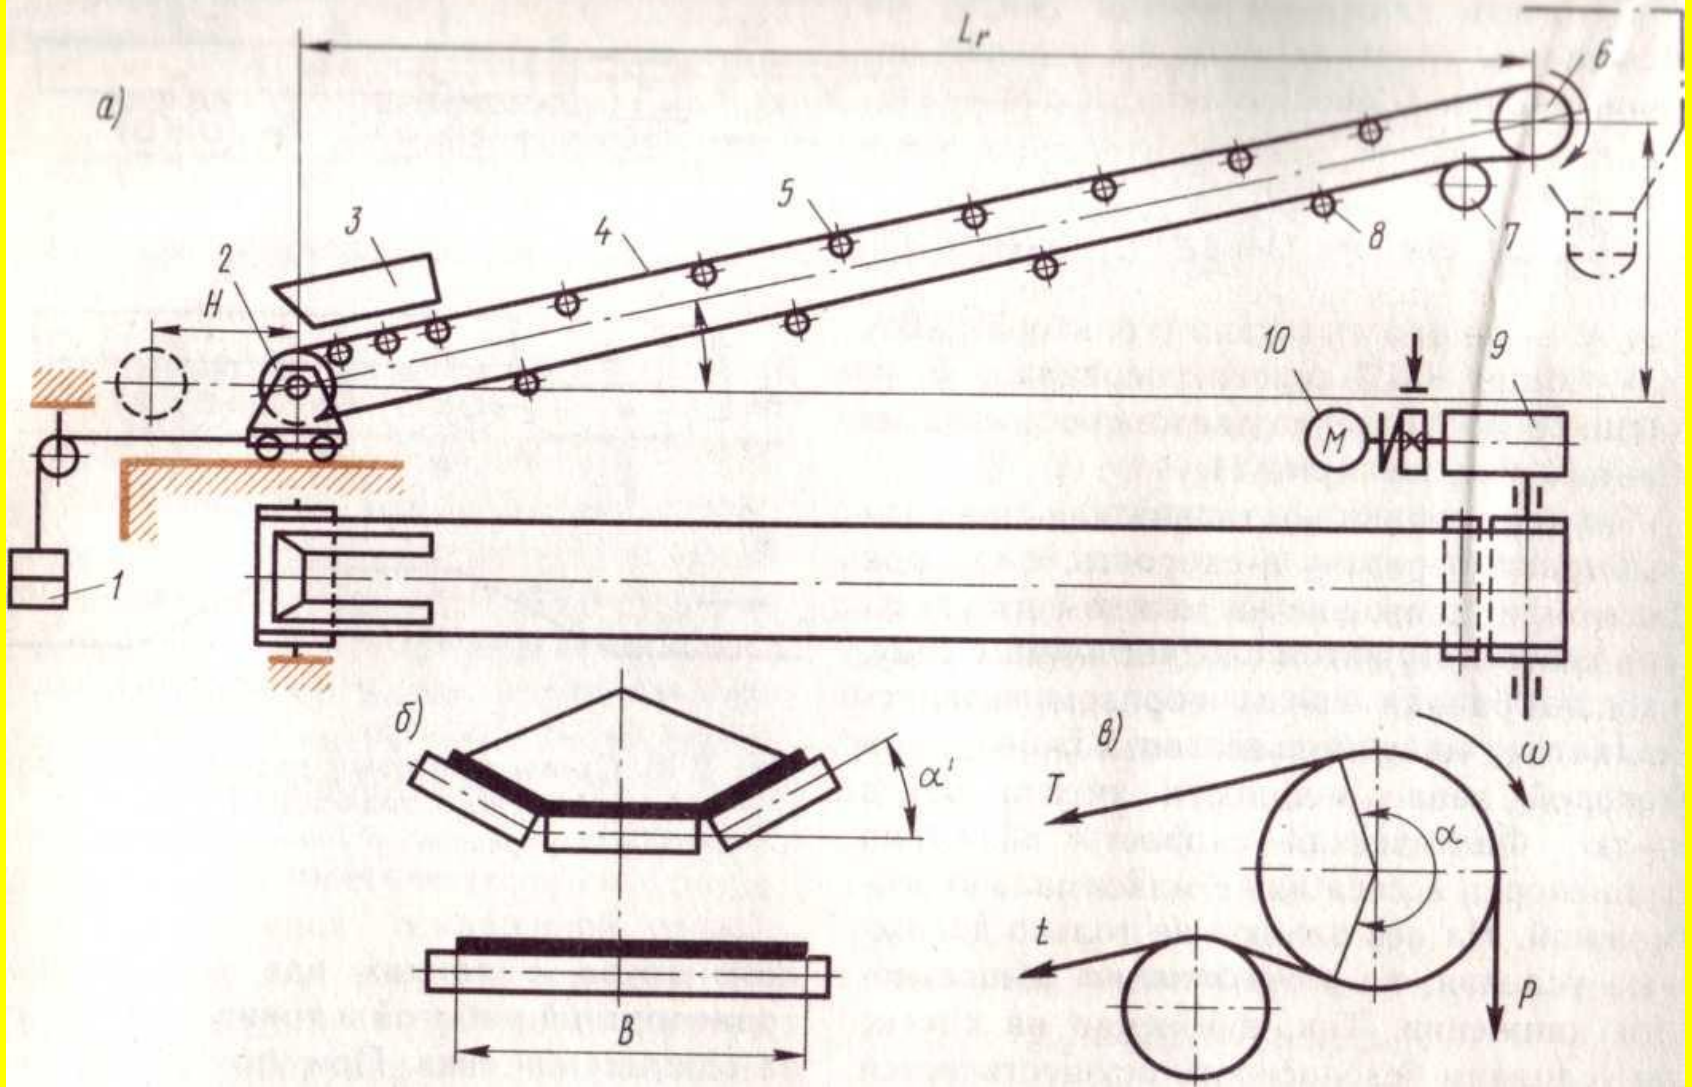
Ленточный конвейер: а) схема конструкции; б - роlikоопоры; в- схема усилий на приводном барабане
